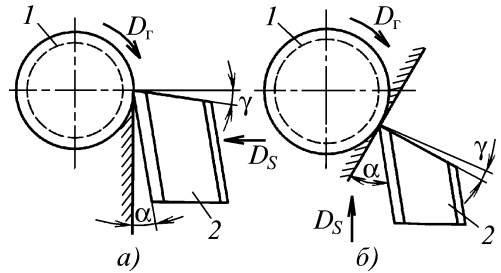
Призматический радиальный фасонный резец, установленный перпендикулярно (*а*) и под углом ω (*б*) к заготовке
